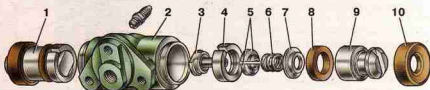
Детали колесного цилиндра: 1 — поршень в сборе; 2 — корпус цилиндра; 3 — упорный винт; 4 — упорное кольцо; 5 — сухари; 6 — пружина; 7 — опорная чашка; 8 — уплотнитель; 9 — поршень; 10 — защитный колпачок
